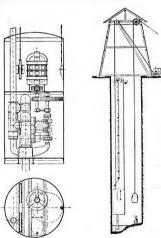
Drillings-Kolbenpumpe von Siemens & Halske, Berlin.
